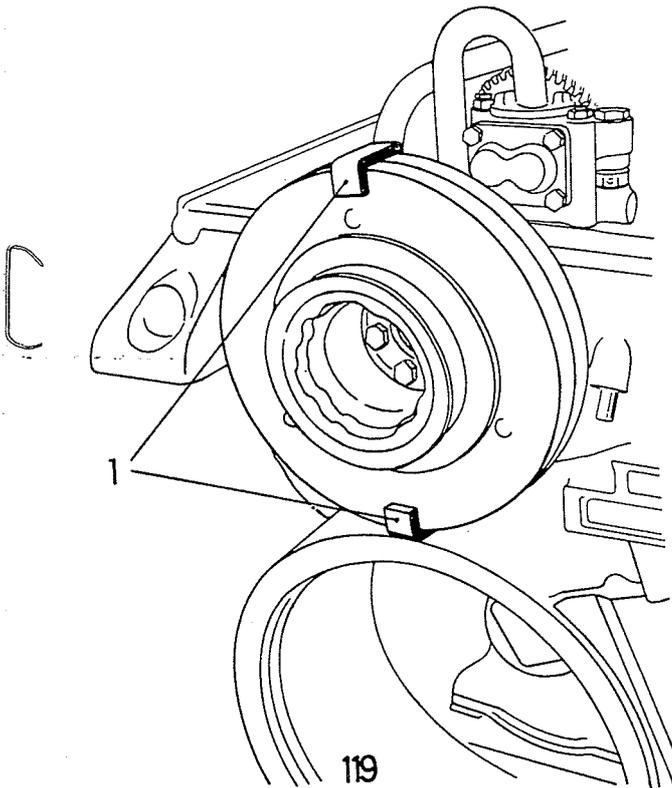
Montageklammern für Schwingungsdämpfer F/A 8L 614
